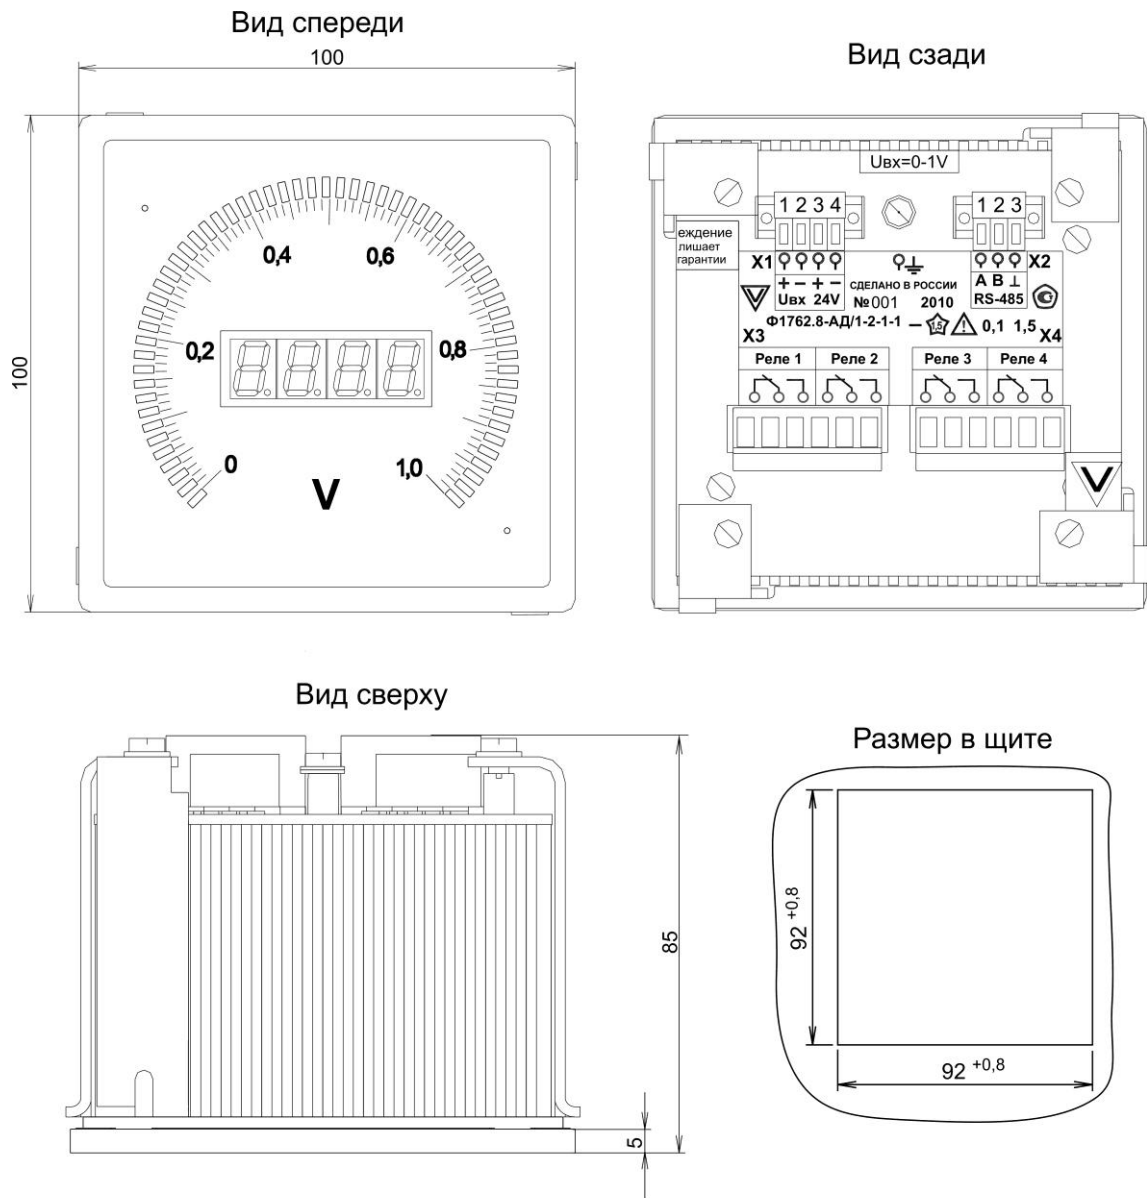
Внешний вид и конструктив приборов, разметка щита и схема подключения приборов Ф1762.8–АД/1–х–х–1 и Ф1762.8–АД/1–х–х–2
